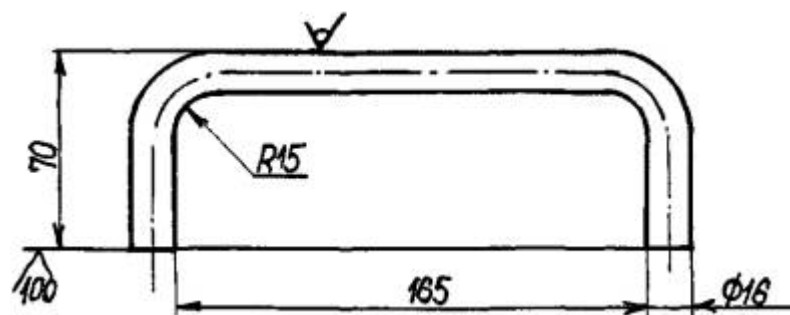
Конструкция и размеры ручки для люка-лаза
